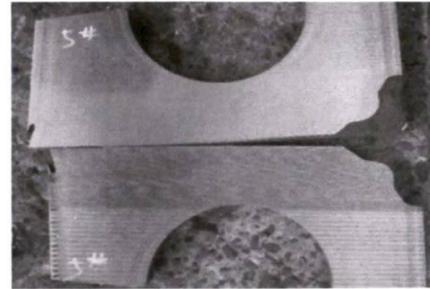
轴承座螺栓孔及油孔切面显示无铸造缺陷
